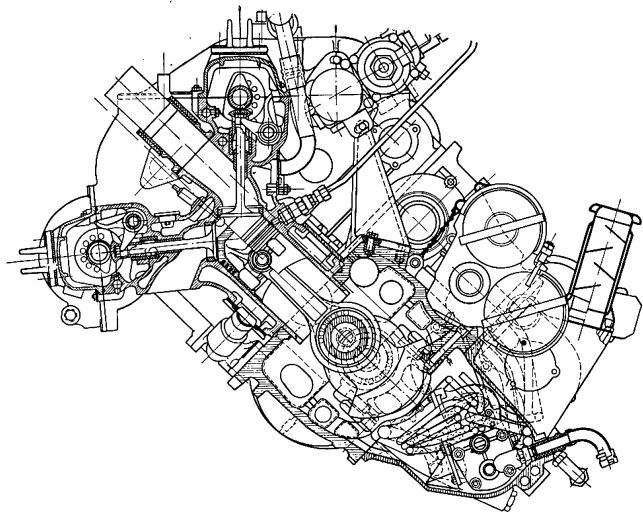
Поперечный разрез двигателя автомобиля «Мерседес-Бенц» «SLR»
